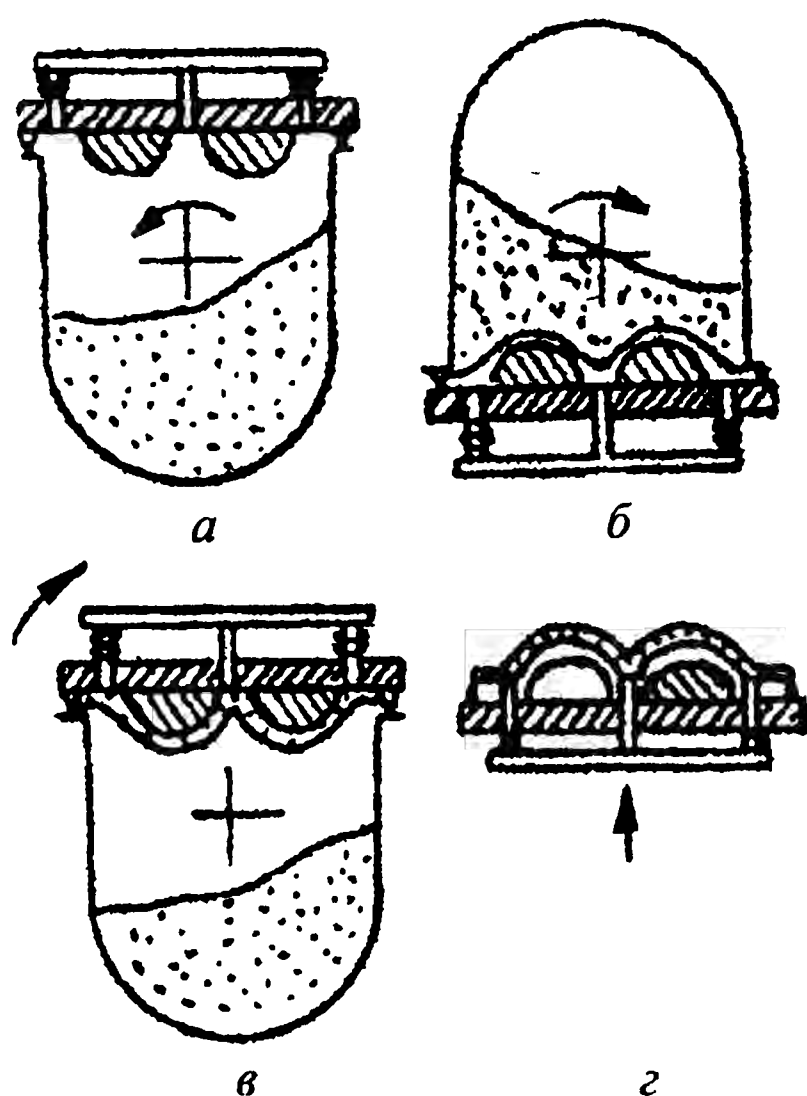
Схема изготовления оболочковой формы с помощью поворотного бункера
